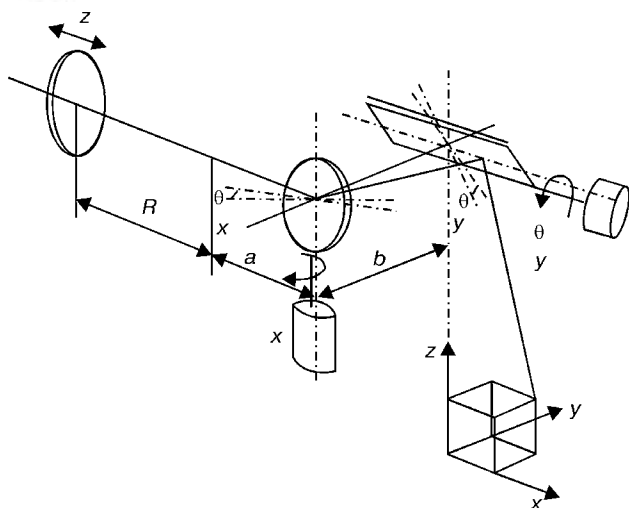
Схема сварки с дистанционным наведением лазерного луча
